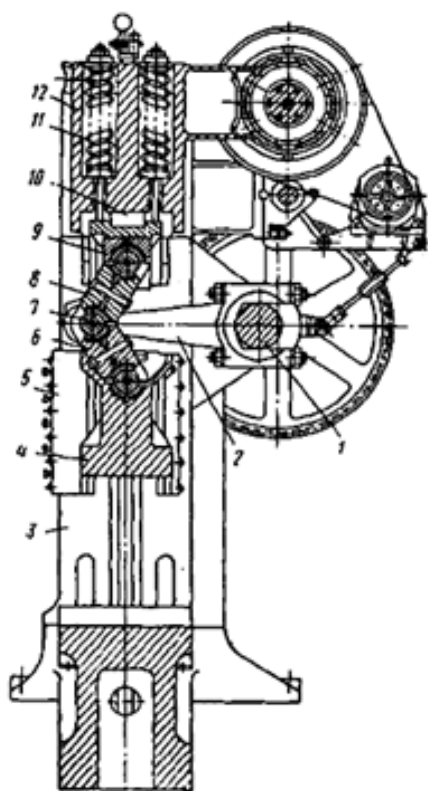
Чеканочный пресс: 1-кривошипный вал, 2-шатун, 3-станина, 4-ползун, 5-направляющие, 6-нижнее звено, 7-шарнир, 8-верхнее звено, 9-опора верхнего звена, 10-клин, 11-подпружиненная стяжка, 12-верхняя траверса
